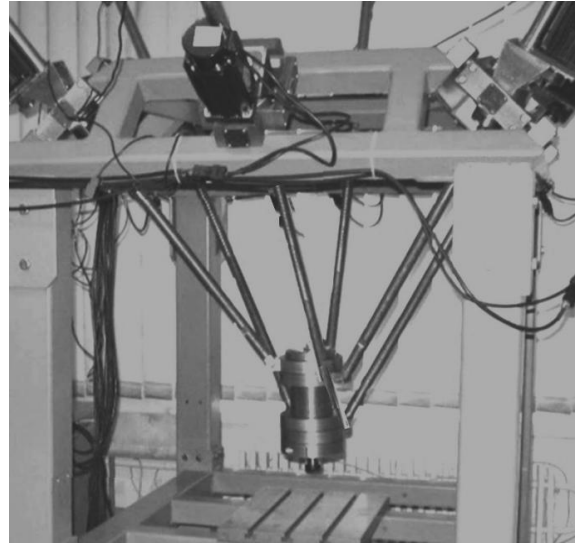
Верстат із надлишковими приводами для дослідження процесу різання заготовок абразивним інструментом
